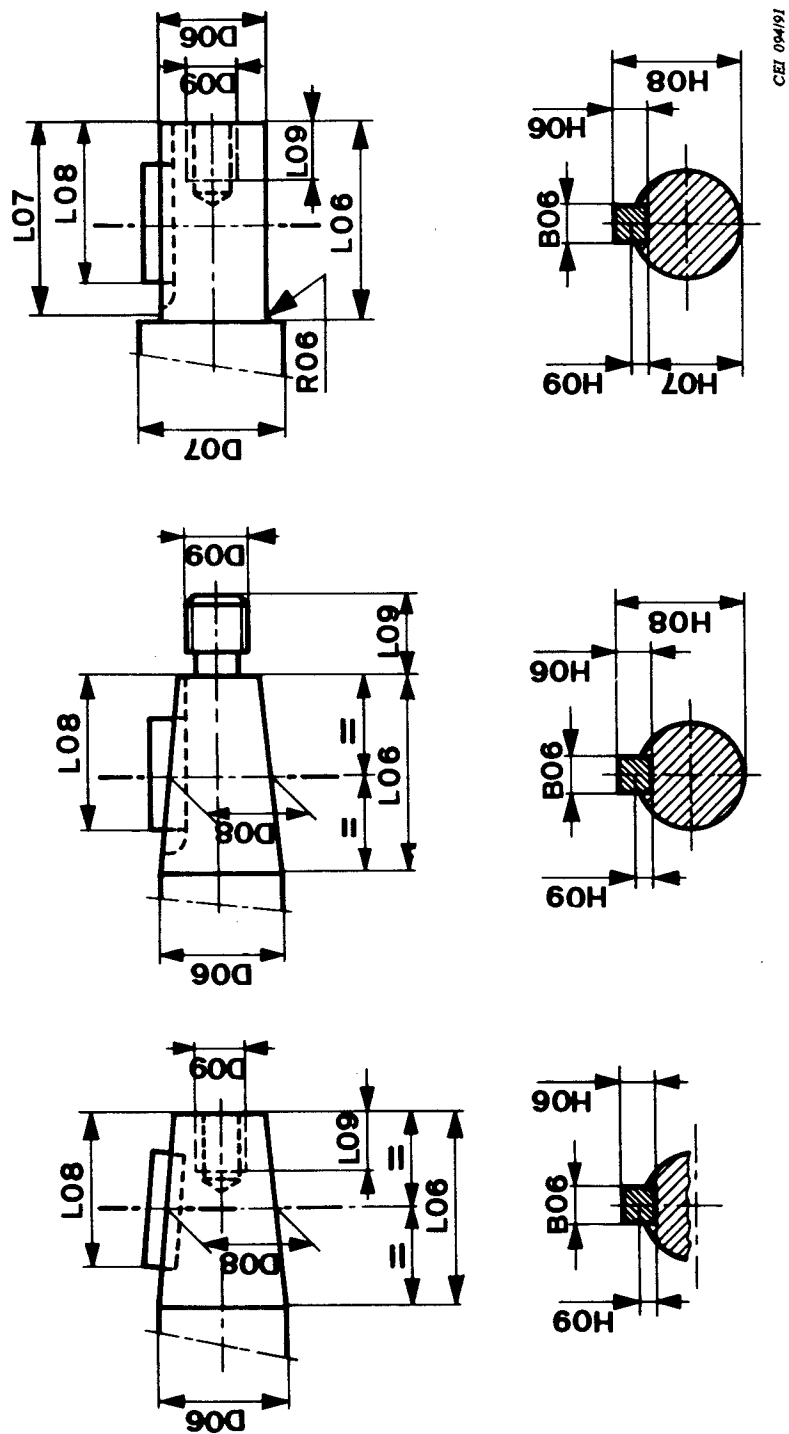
Dimensions de montage de l'arbre côté N de la machine
